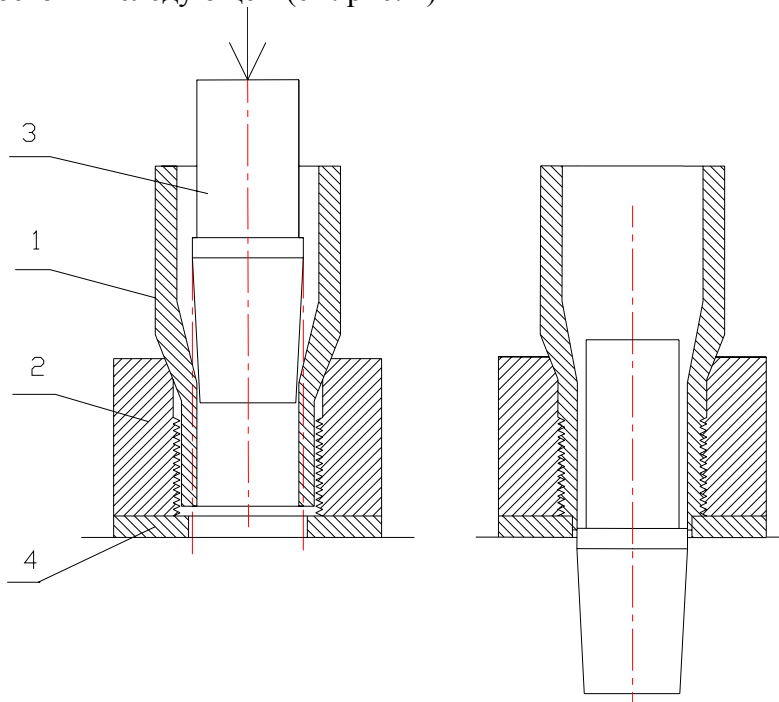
Схема штамповки резьбы на ниппельном конце переводника
